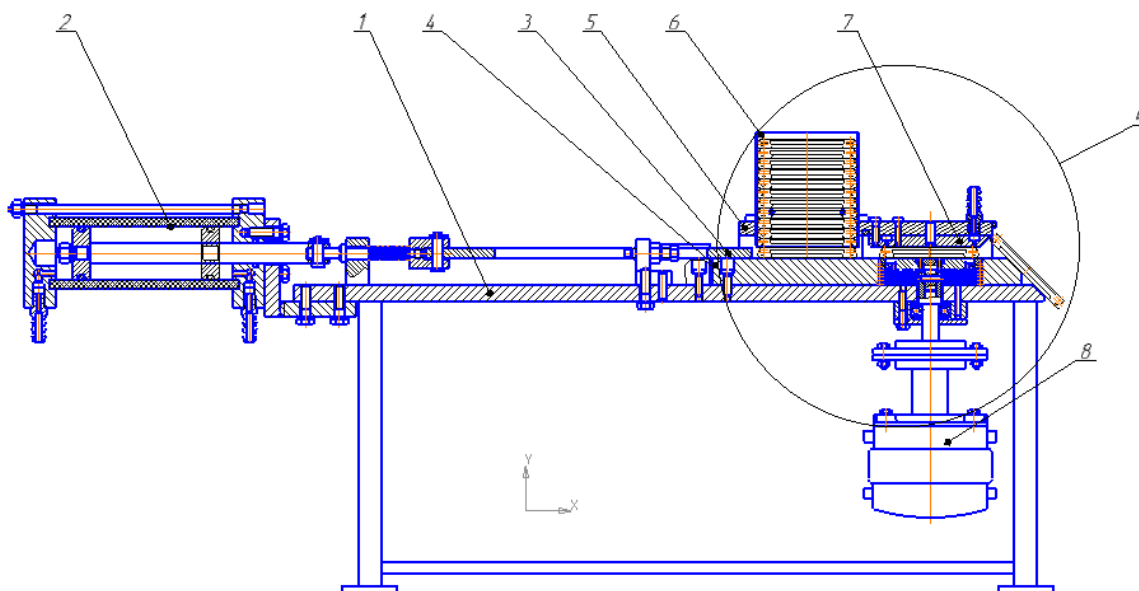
Схема автоматической линии для нанесения смазки
